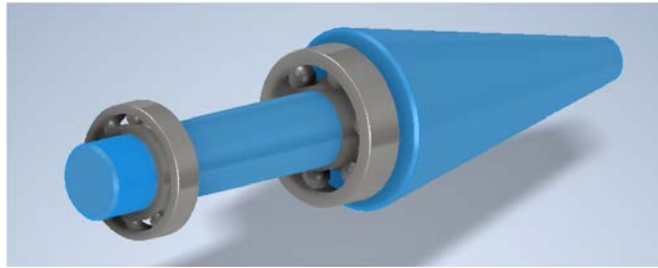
Rodamientos sobre eje de rodillo cónico.
